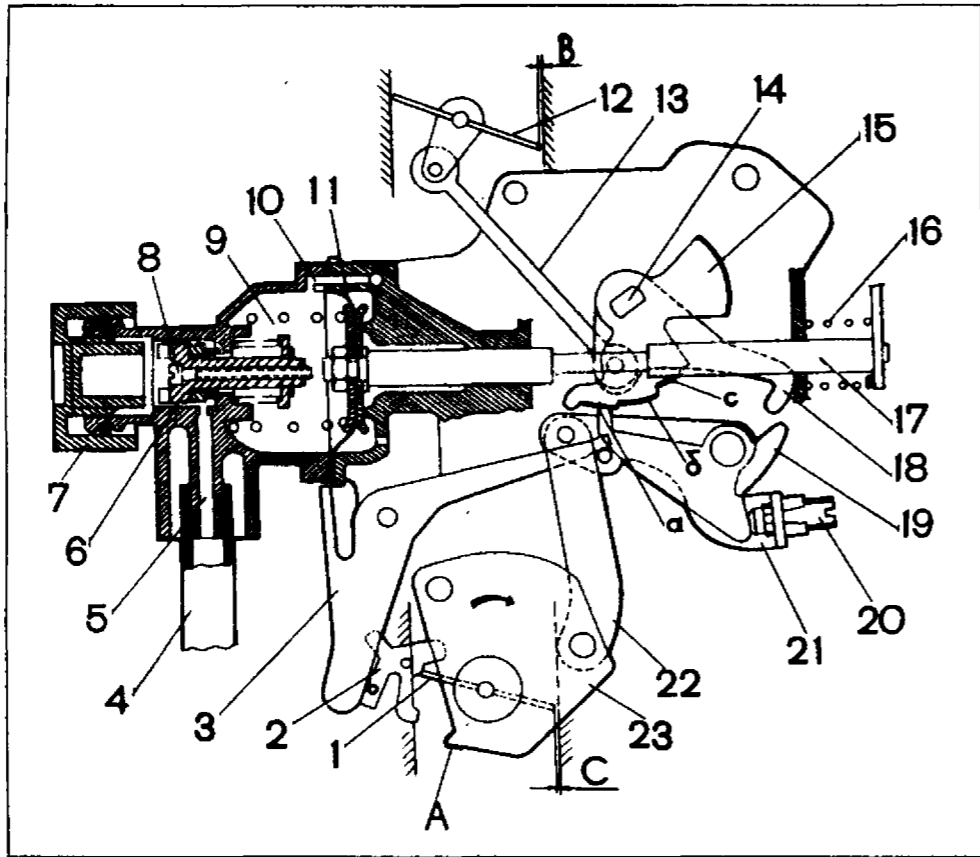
Полуавтоматическое пусковое устройство карбюратора: 1 — дроссельная заслонка первой камеры; 2 — рычаг блокировки второй камеры; 3 — рычаг привода блокировки; 4 — шланг к ресиверу; 5 — штуцер; 6 — плунжер; 7 — упор регулировки второй ступени; 8 — регулировочный винт; 9 — диафрагменная полость; 10 — воздушный канал из задрросельного пространства карбюратора; 11 — диафрагма пускового устройства; 12 — воздушная заслонка; 13 — тяга привода воздушной заслонки; 14 — ось пускового устройства; 15 — кулачок; 16 — пружина штока; 17 — шток диафрагмы пускового устройства; 18 — крючок блокировки второй камеры; 19 — рычаг упора; 20 — регулировочный винт приоткрывания дроссельной заслонки первой камеры; 21 — рычаг приоткрывания дроссельной заслонки; 22 — тяга приоткрывания дроссельной заслонки; 23 — рычаг управления дроссельными заслонками; А — упор блокировки второй камеры; В — пусковые зазоры у воздушной заслонки; С — пусковой зазор у дроссельной заслонки; а, б, с — первая, вторая и третья ступени кулачка
